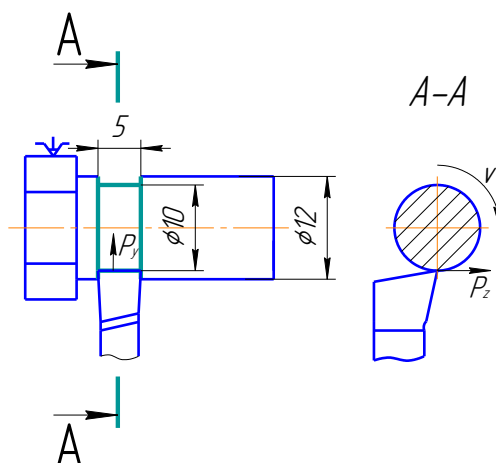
Схема технологической накладки станка на позиции IV
